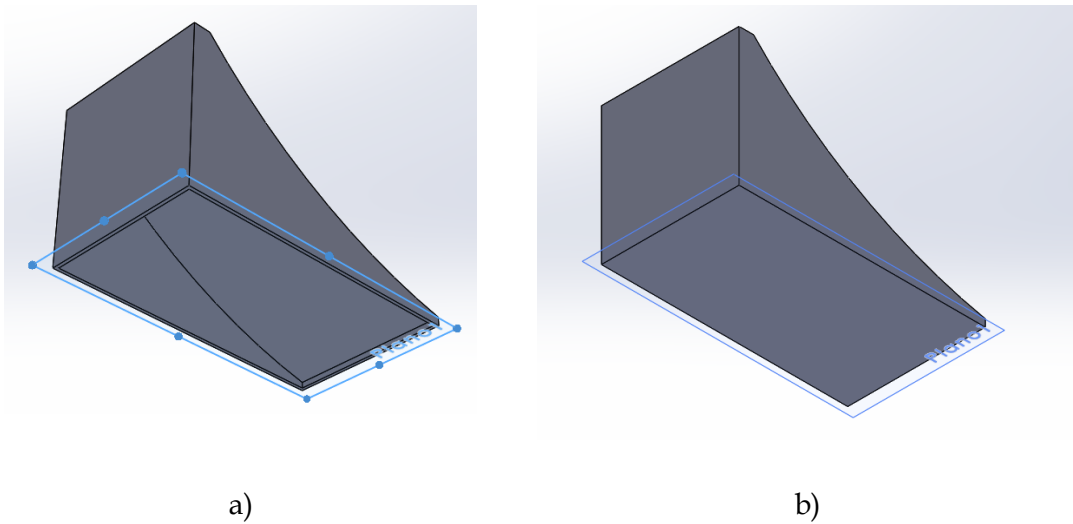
a) Definición de un plano coincidente con la base, b) operación de extrusión con una profundidad de 2mm utilizando las aristas croquizadas sobre el plano.
